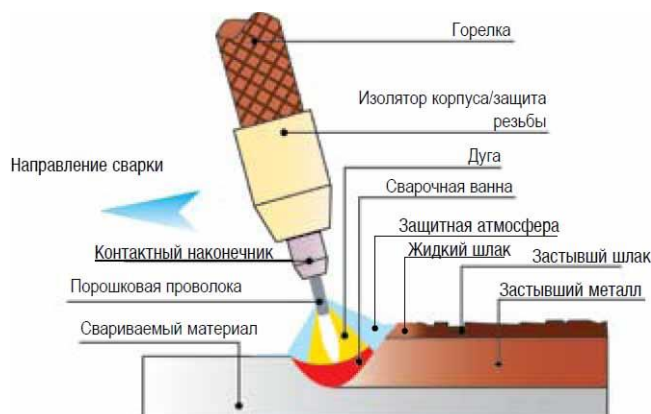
Эскиз механизированной сварки самозащитой порошковой проволокой
